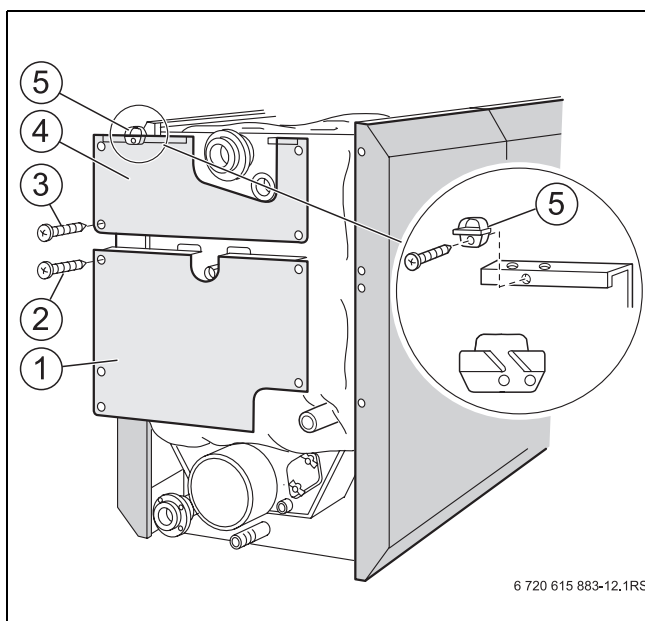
Zavěšení bočních stěn a připevnění kabelu hořáku
